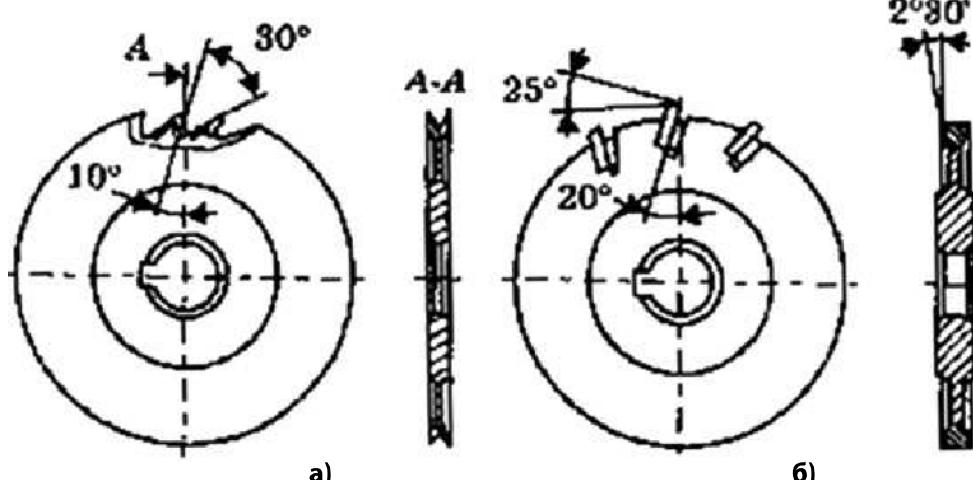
Дисковые пилы: а) с разводом зубьев; б) со вставными зубьями
